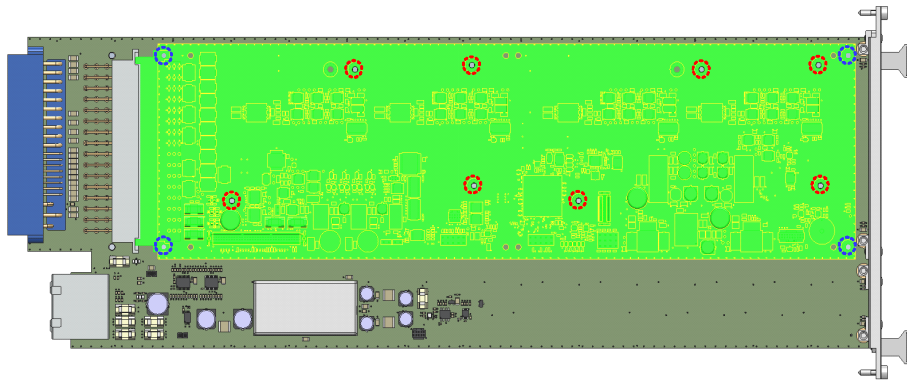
Lage der Bohrungen auf der ES5372.1-B mit eingebauter ES4455.2
